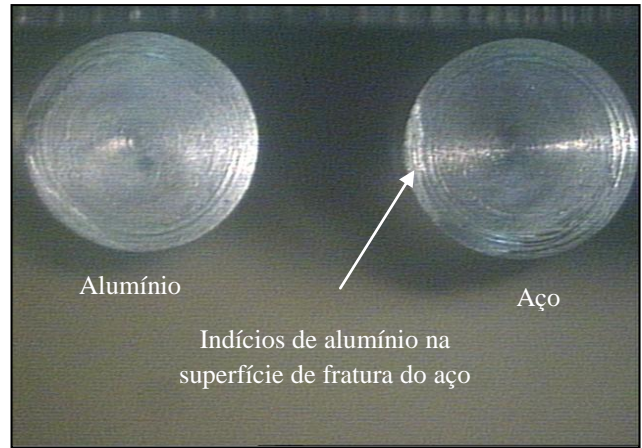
Superfície de fratura das soldas com preaquecimento.
